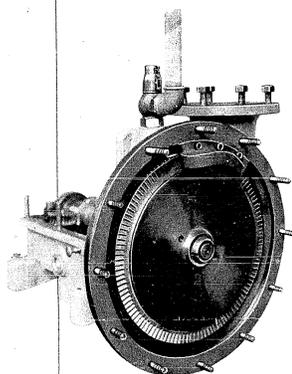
Mehrfach axial beaufschlagtes Laufrad
